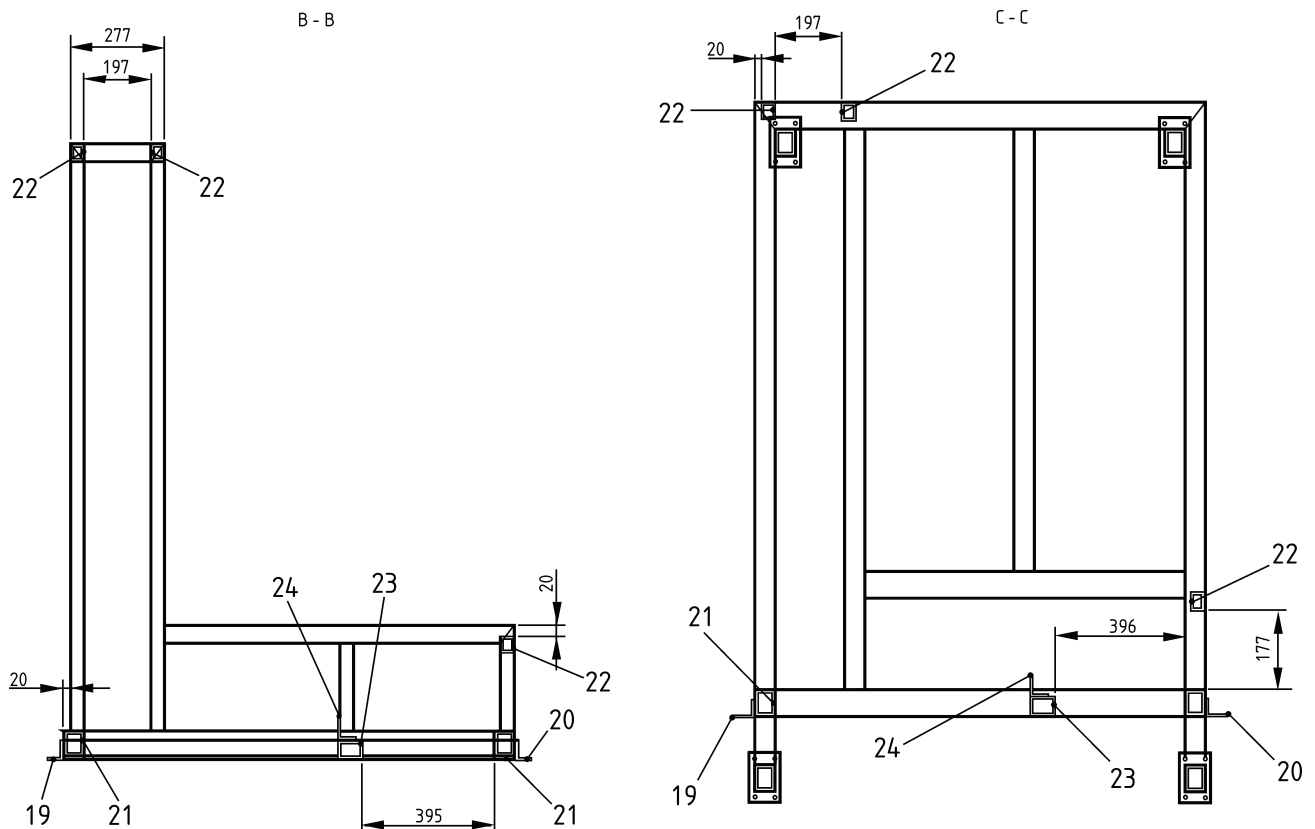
Probenträgerwagen, geschweißte Teile, Bodenplatte
